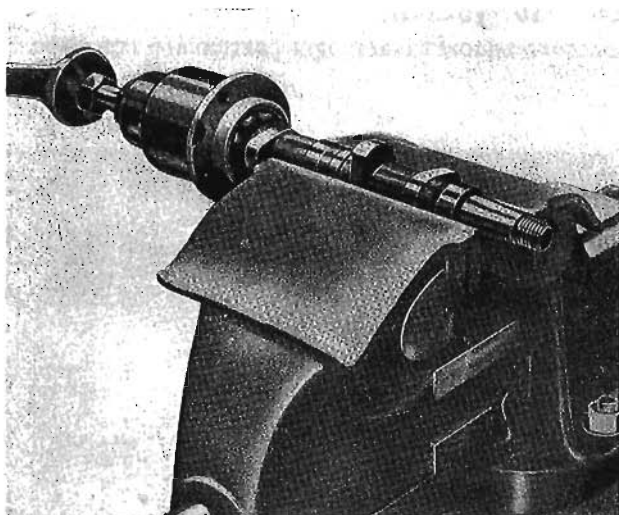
Smontaggio della boccia dentata per albero mediante l'estrattore A 227006.
